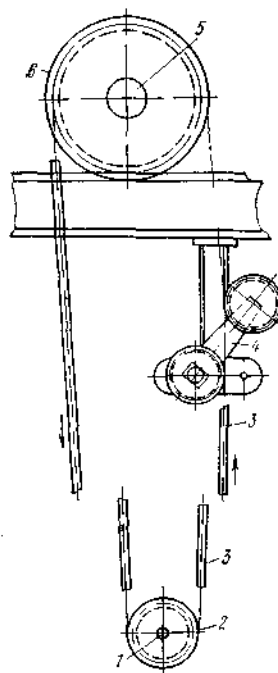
Схема привода двухподъемной жаккардовой машины:
